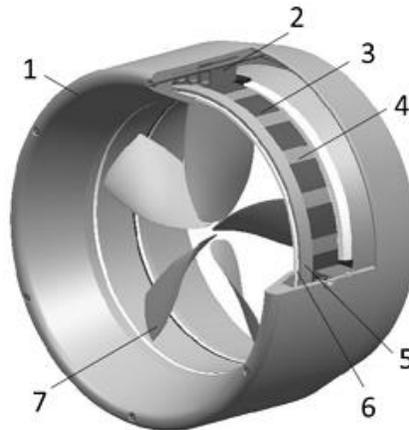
Туннельный движитель (1 – кольцевое крыло, 2 – статор, 3 – магниты ротора, 4 – ярмо ротора, 5 – вкладыш подшипника, 6 – водоподшипник, 7 - винт).
